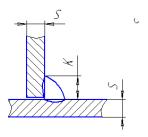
Соединение Т1 - Δ 3 по ГОСТ 14771-76, сварной шов №1
